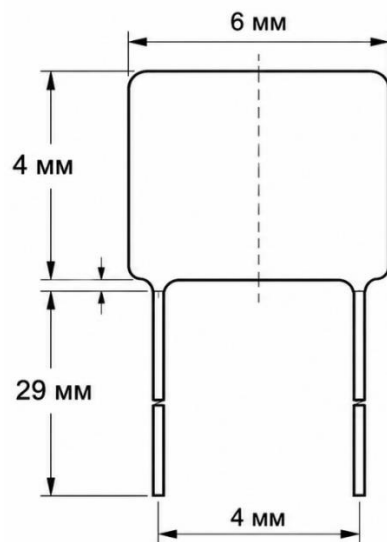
Габаритні розміри постійного резистора типу С2-33
